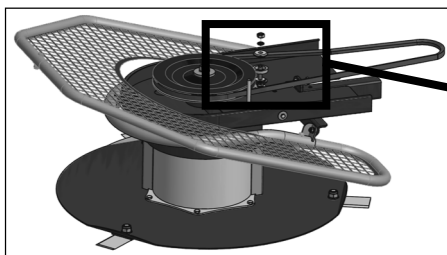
a,b Suport pentru inelele distanțiere (pt. a evita pierdere lor)
